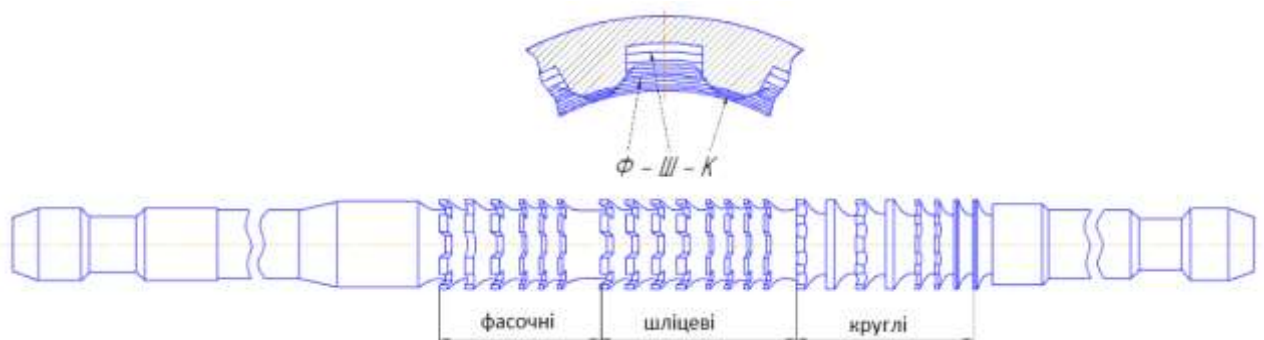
Комбінована шліцьова протяжка 4 типи
